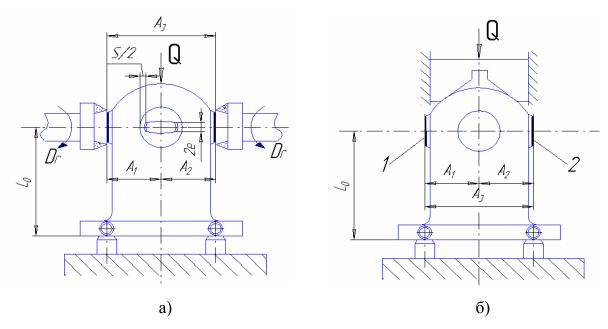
Два варианта базирования корпуса: а — на основную плоскость и отверстие; б — на основную плоскость и наружную поверхность заготовки: 1, 2 — обрабатываемые поверхности
